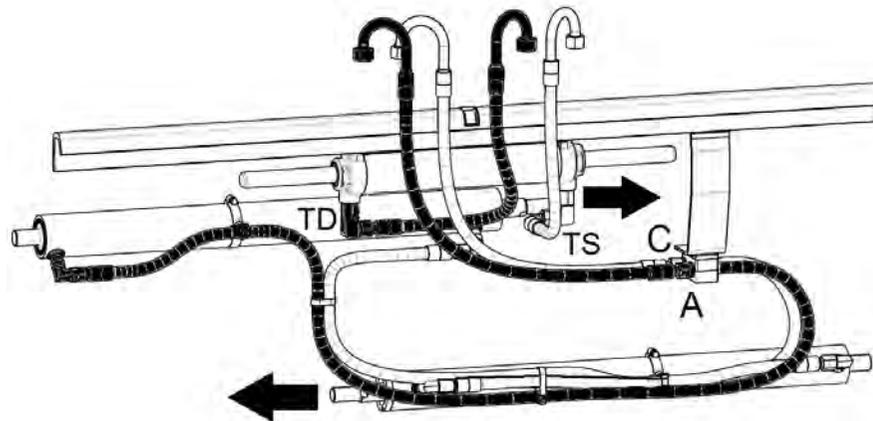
Impianto idraulico per versioni con traslazione separata con posizione ingressi alimentazione forche centro telaio
